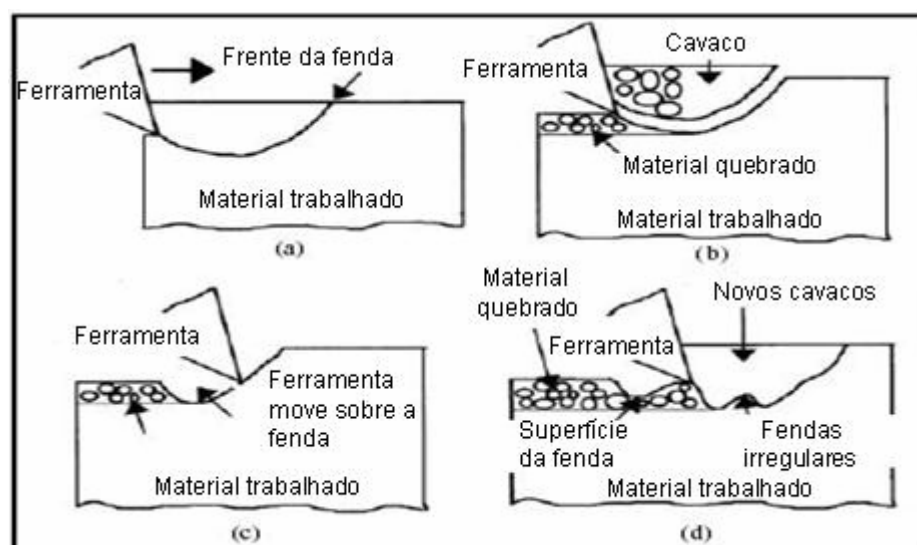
Desenho esquemático da formação de cavacos para ferros fundidos [23].
